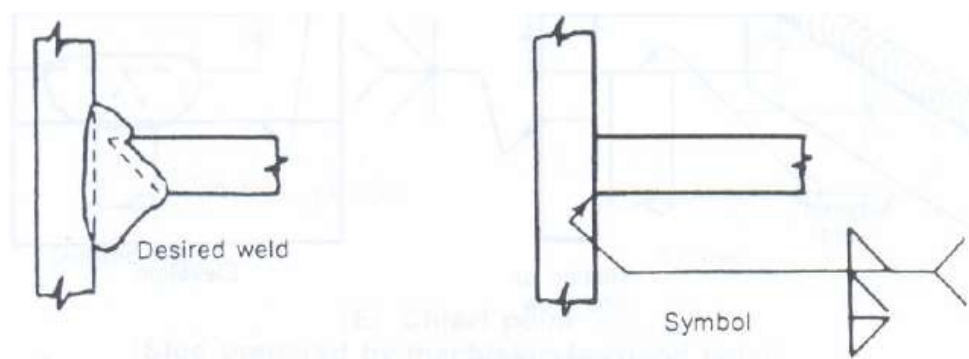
Soldadura tipo ranura simple y doble filete (1).
